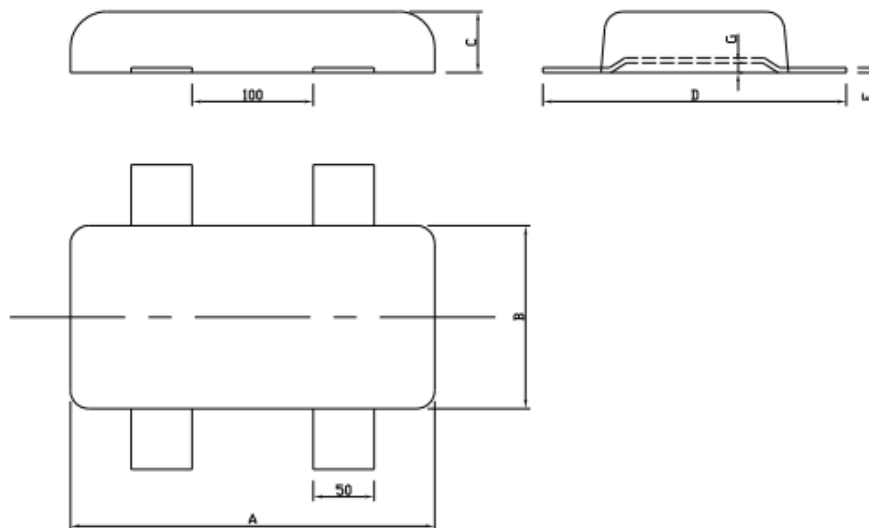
Ánodos de Zinc para cascos de buques (Del tipo soldadura w /doble inserto)
